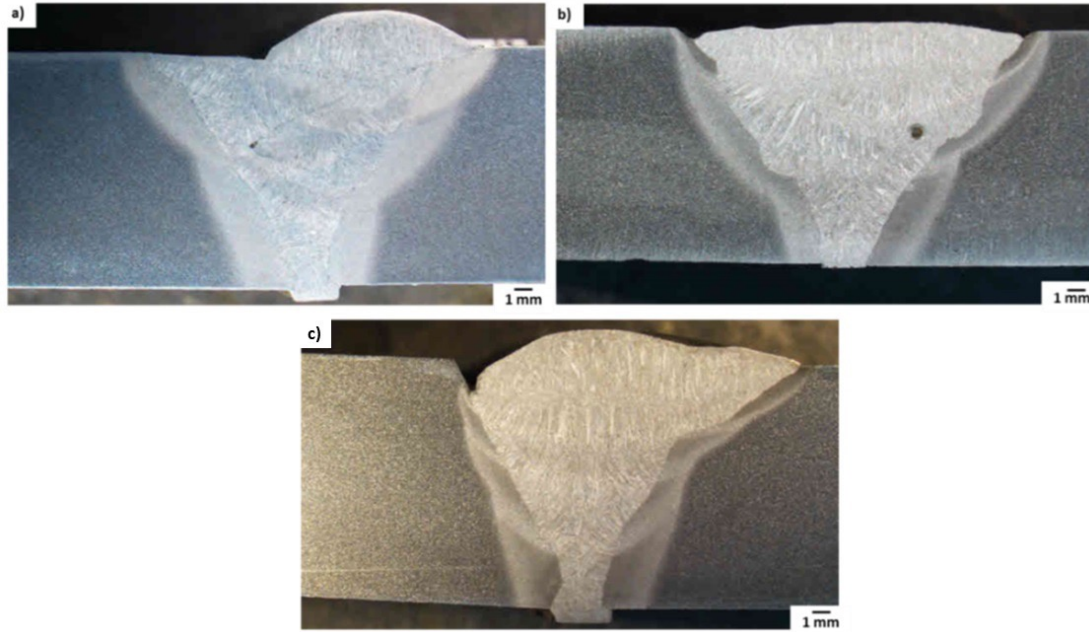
Macrográficas de uniones soldadas a tope en condición de soldadura B (159 A, 23 V, velocidad de soldadura de 31.5 cm/min) utilizando soldadura robótica GMAW y diferentes movimientos de soldadura a) lineal, b) sinusoidal y c) triangular [12].
